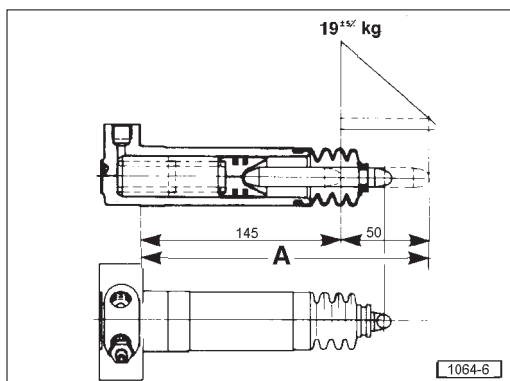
Cilindro hidráulico de mando del grupo embrague.
